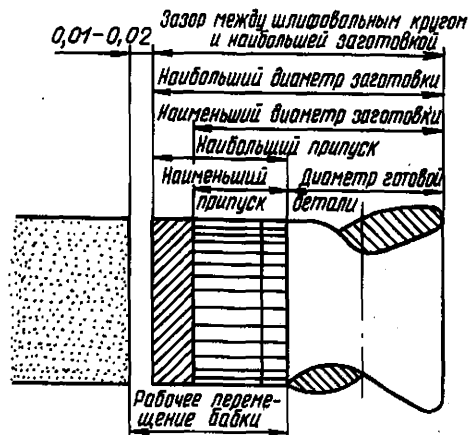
Схема рабочего перемещения шлифовальной бабки
